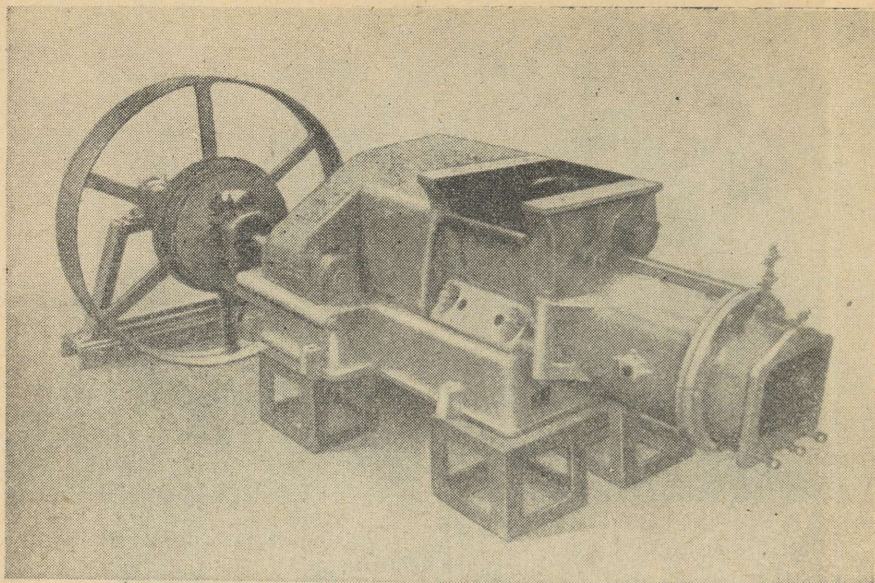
Ленточный вакуум-пресс со ступенчатым шнеком, диаметр цилиндра 300 мм.
